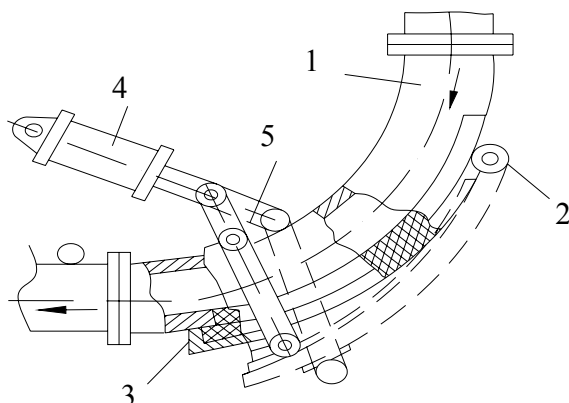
Устройство для аварийного сброса закладочной смеси из вертикального трубопровода: 1 – колено трубопровода; 2 – шарнир клапана; 3 – клапан; 4 – пневмопривод; 5 – тяга пневмопривода
